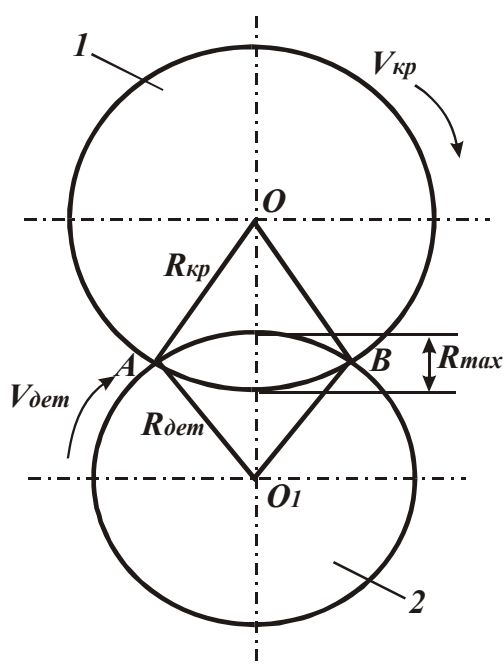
Расчетная схема круглого наружного шлифования: 1 – круг; 2 – деталь.
